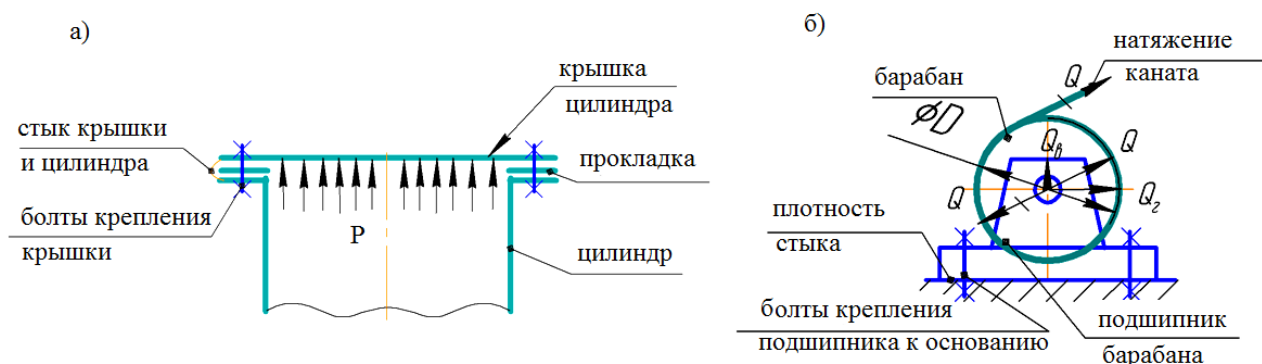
Ситуации, приводящие к нагружению болтов центральной отрывающей силой: а) крепление крышки цилиндра; б) крепление подшипников барабана.
